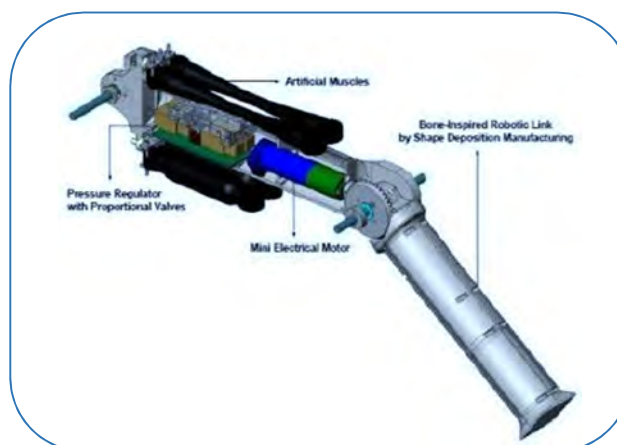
Diseño DM2 de la Universidad de Stamford.
